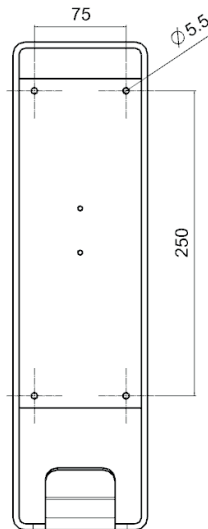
ESTRUTURA DO SUPORTE DE CONECTOR
